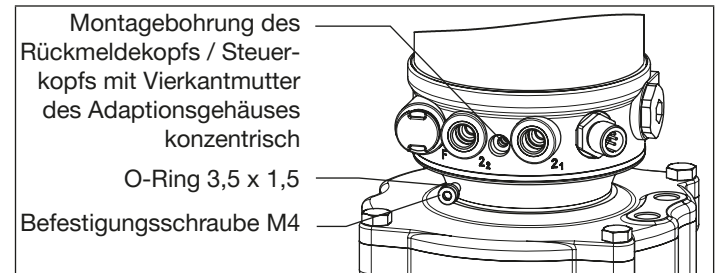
Befestigung Rückmeldekopf / Steuerkopf
